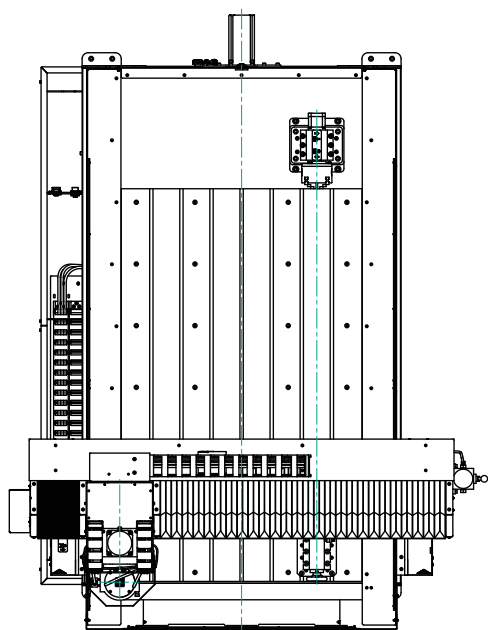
Габаритные размеры фрезерного станка с ЧПУ REINER ME140M.
